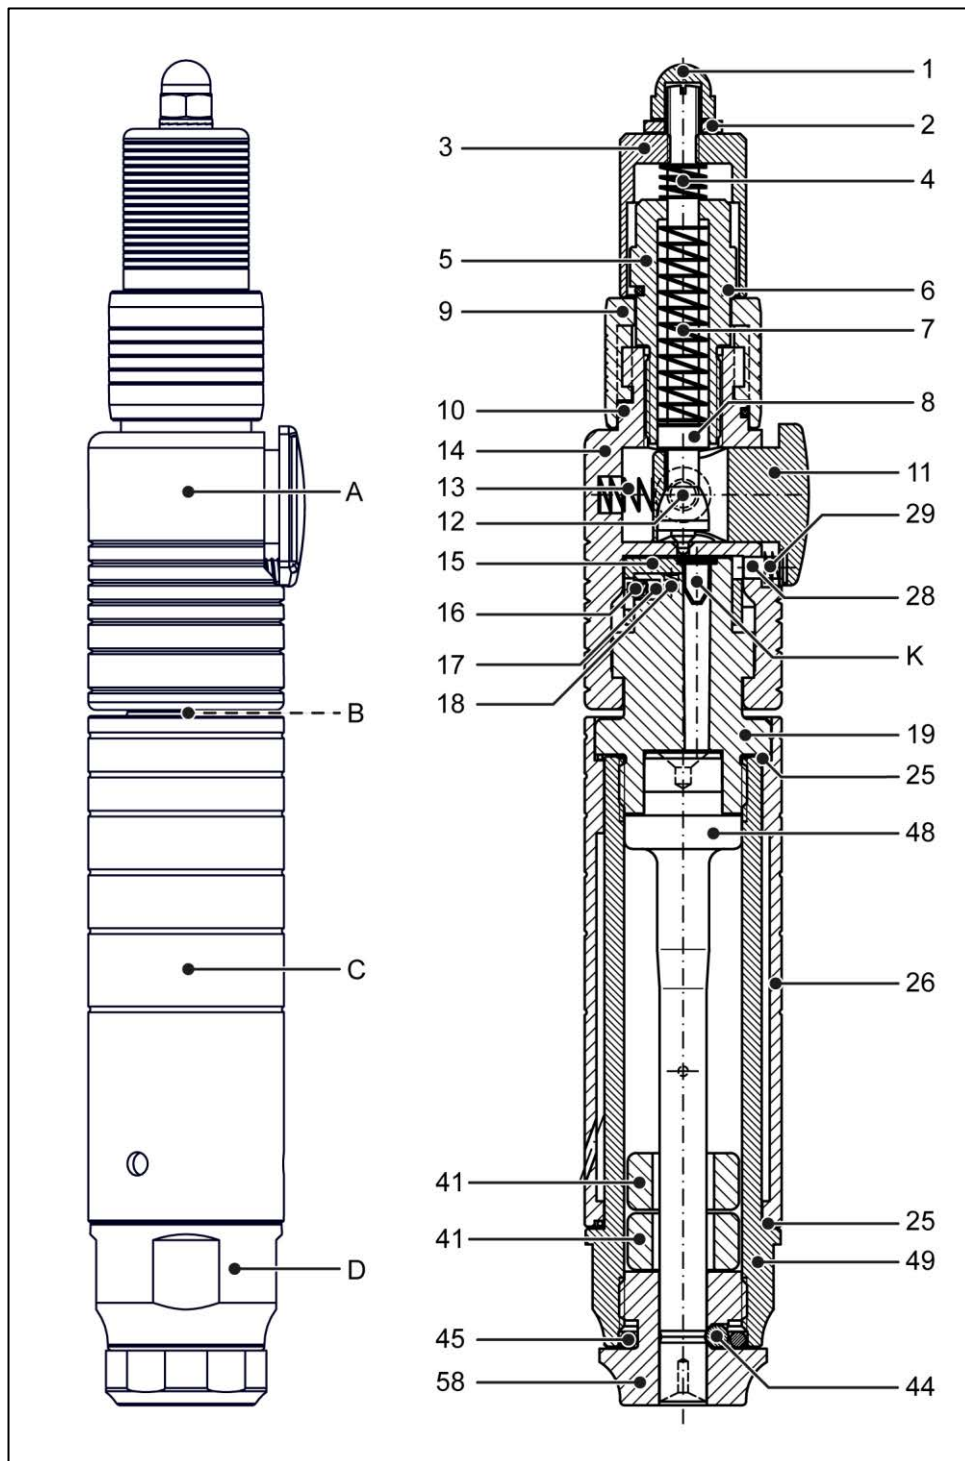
Baugruppen/Bauelemente Typ KK
